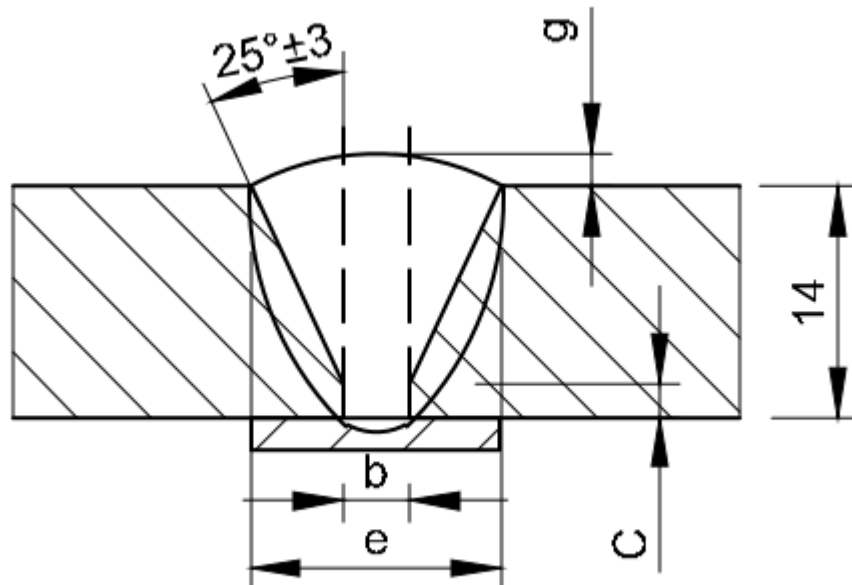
Конструктивний розріз підготовки кромки та зварного з'єднання
